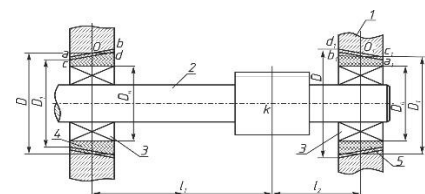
Общая схема установки вращающегося вала с несимметричным центром масс
